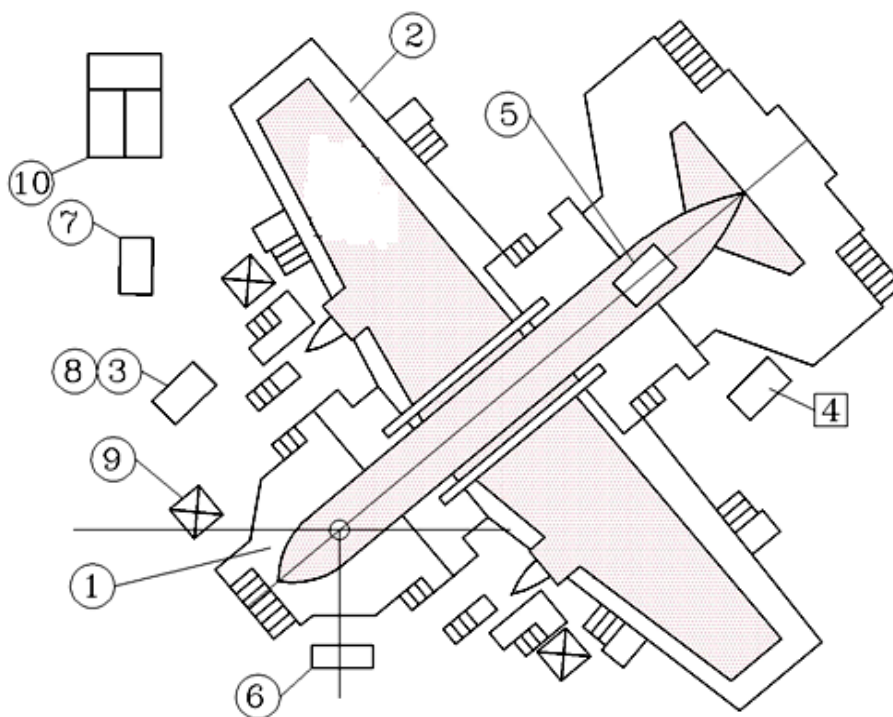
Стенд монтажа силовых установок, испытания трубопроводных систем на герметичность, прокладки и прозвонки цепей ЭРАНО: 1 – стремянки фюзеляжные; 2 – стремянки подкрыльевые; 3 – стенд для промывки трубопроводов и испытания гидросистемы на герметичность; 4 – стенд для испытаний трубопроводов топливной и масляной систем; 5 – стенд комплексной отработки гидросистемы; 6 – стенд для испытаний на герметичность опрессовки СКВ; 7 – стенд для заливки и отработки гидросистемы; 8 – стенд для испытаний на герметичность кислородной системы и заправки кислородных баллонов; 9 – стенд для испытаний на герметичность ППС; 10 – стенд для контроля системы управления самолетом СКСУ-114
